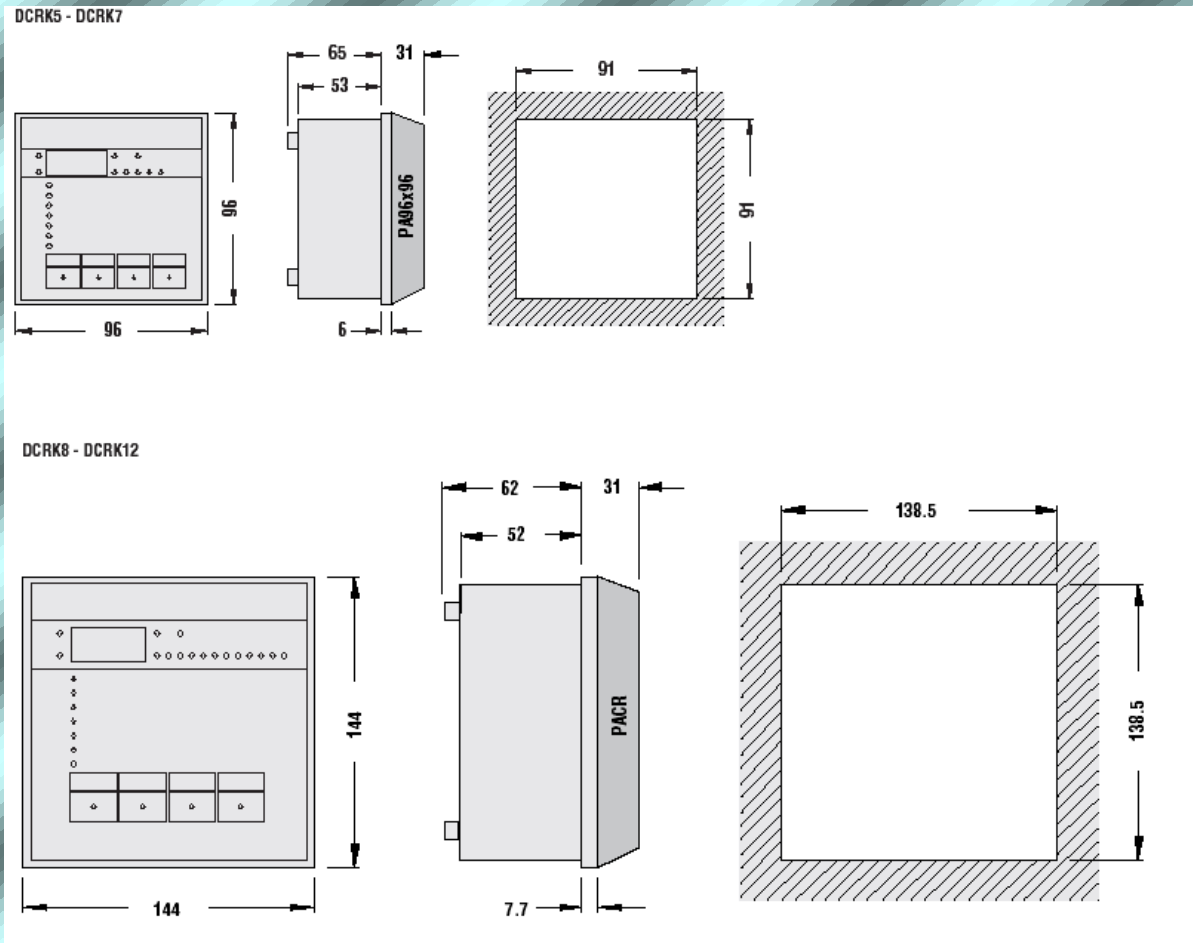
Внешний вид передней панели и габаритные размеры DCRK 5-12.
